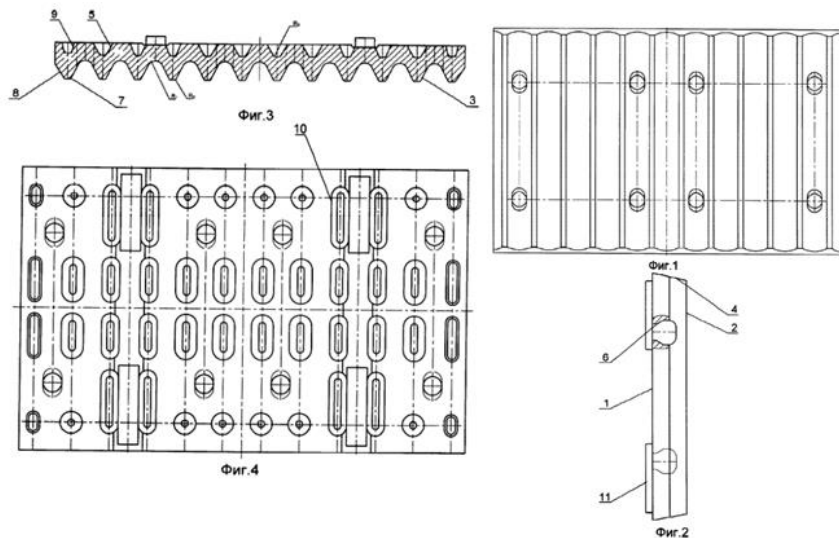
Предлагаемая плита дробящая щековой дробилки
